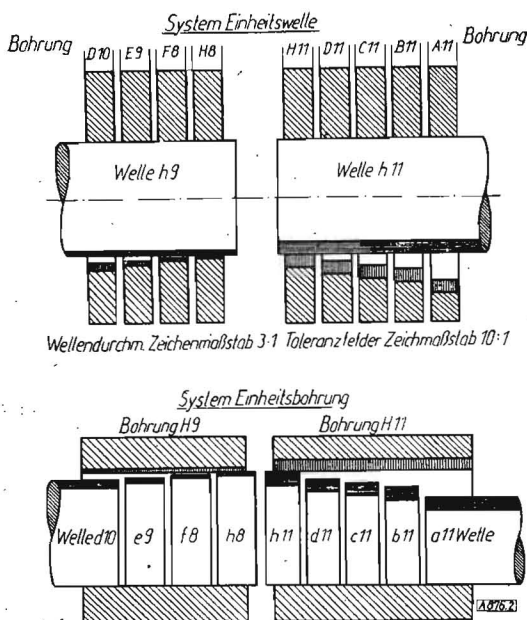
Lage der Toleranzfelder für die Landmaschinenfertigung wichtigsten Passungen
